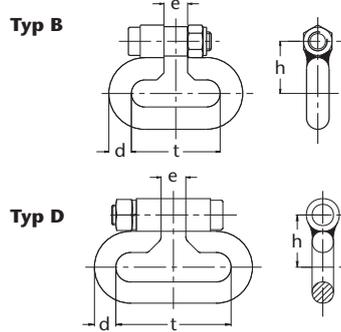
HEKO Kettenschloß Typ B mit angeschweißter Mutter, Typ D mit loser Mutter
